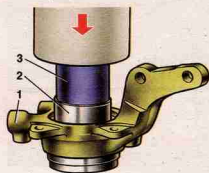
Запрессовка подшипника в поворотный кулак: 1 – поворотный кулак; 2 – подшипник; 3 – оправка
